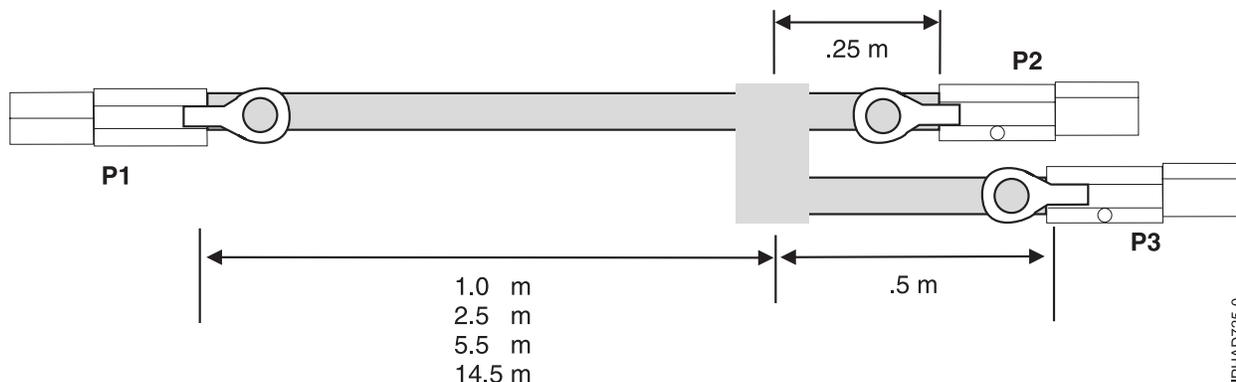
Comprimentos de cabo do conjunto de cabos externos SAS YO
